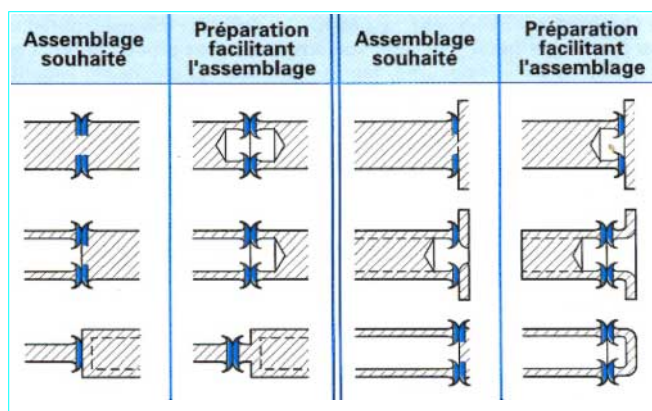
Exemples de préparations de pièces par soudage par friction
